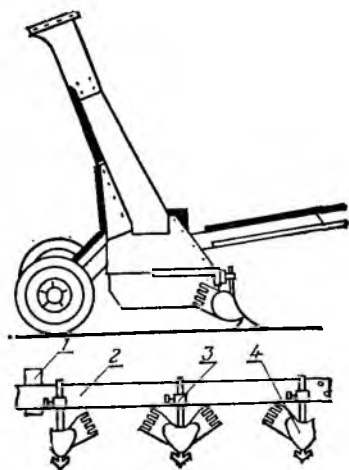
Приспособление к косилке КИР-1,5Б для уборки полеглой ботвы:
